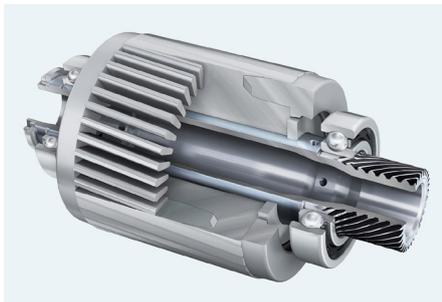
Le rotor à cage d'écurieil est en aluminium et moulé sous pression.
